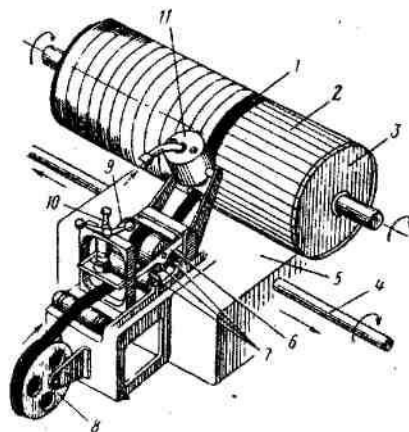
Схема намоточной машины (НМ) на базе токарного станка:
